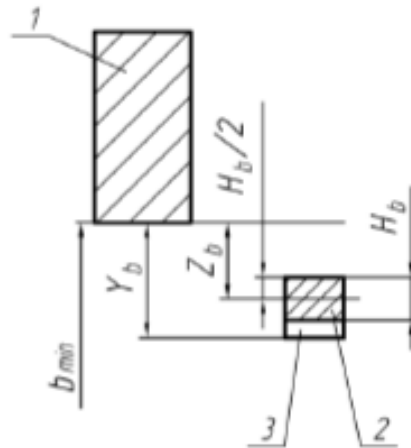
Схеми полів допусків товщини зуба b_k калібра-пробки: 1 –поле допуску розміру b втулки ; 2 – поле допуску на виготовлення калібра-пробки;
